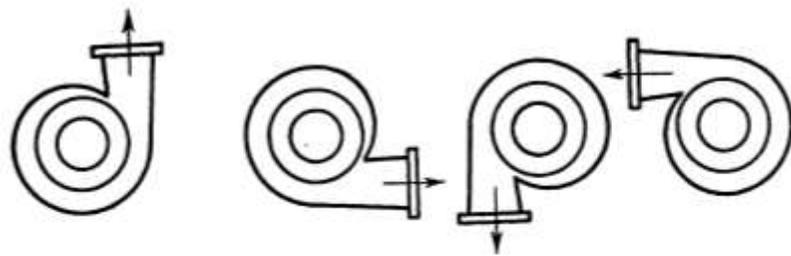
Схемы расположения напорных патрубков консольных центробежных насосов
